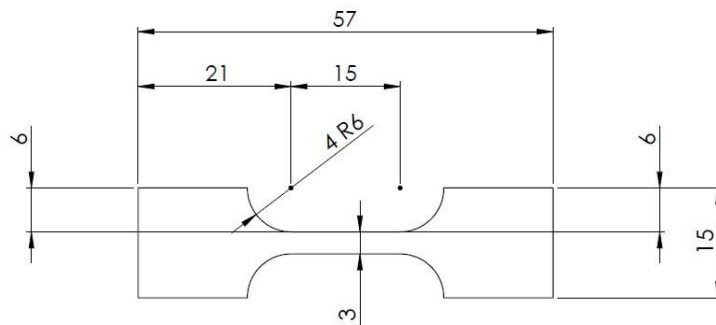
Forme et dimensions des éprouvettes de traction utilisées.
